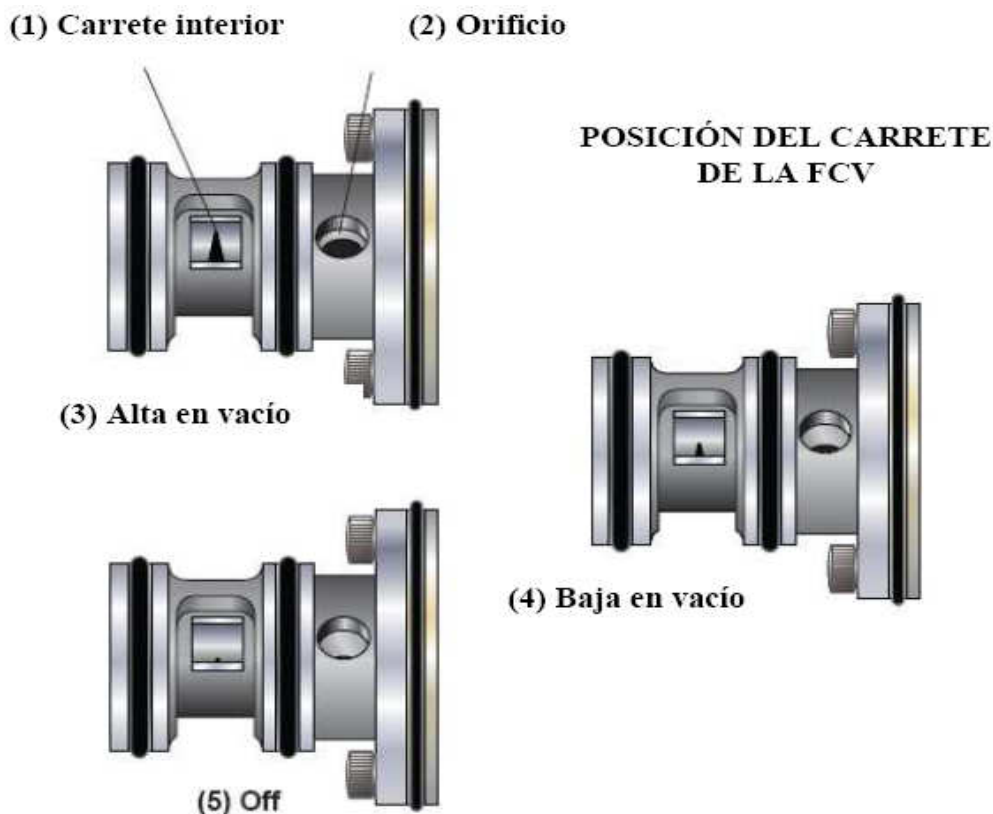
Posición del carrete de la válvula de control de combustible
